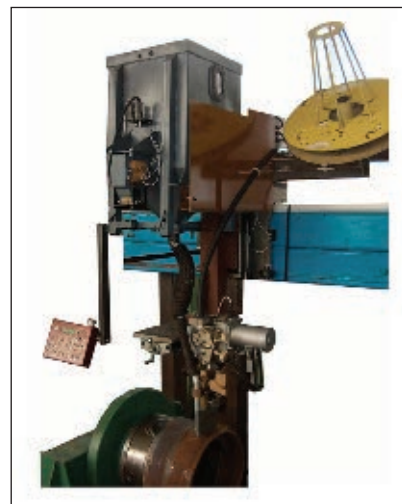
Установка КТС 3-5 для наплавки крановых колес под флюсом
